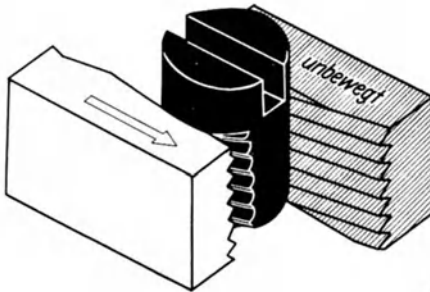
Gewindewalzen. Die Werkzeuge tragen einfache Keillinien in scharfer Profilausbildung.
